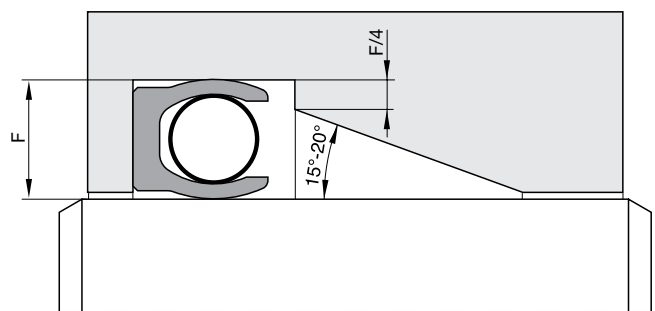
Установка закрытой посадочной канавки в режиме штока с конусным исполнением
